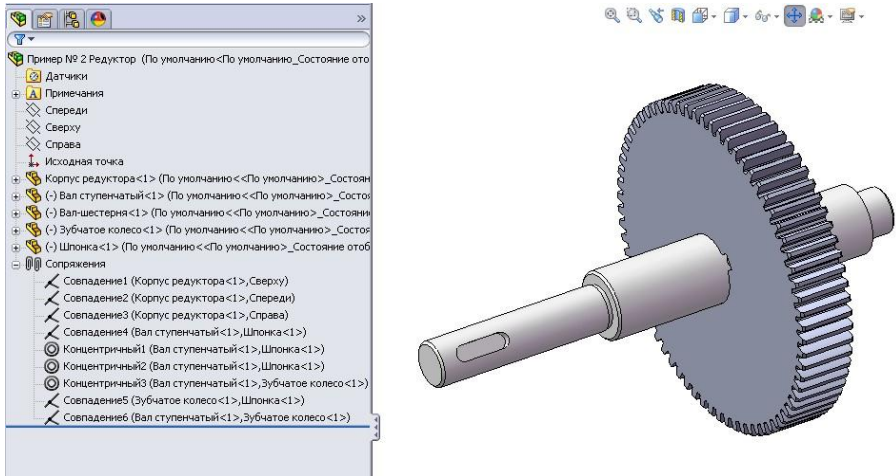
Зубчасте колесо розміщене на валу
